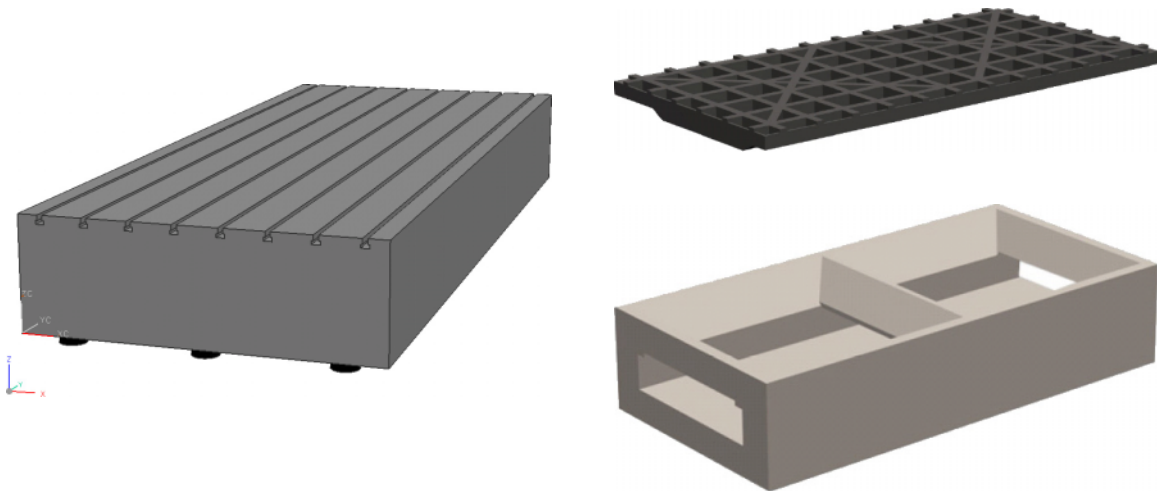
Links: CAD-Modell der Aufspannplatte im Maschinenlabor, die als Grundkörper für den Aufbau der Prototypmaschine genutzt wird. Rechts: Konzeptstudie für ein Universal-Maschinenbett, bestehend aus einer Basis aus Mineralguss sowie einer aufgesetzten Gitterplatte aus Stahl zur Befestigung der Module.
